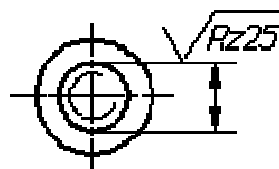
Пример обозначения шероховатости наружной резьбы
